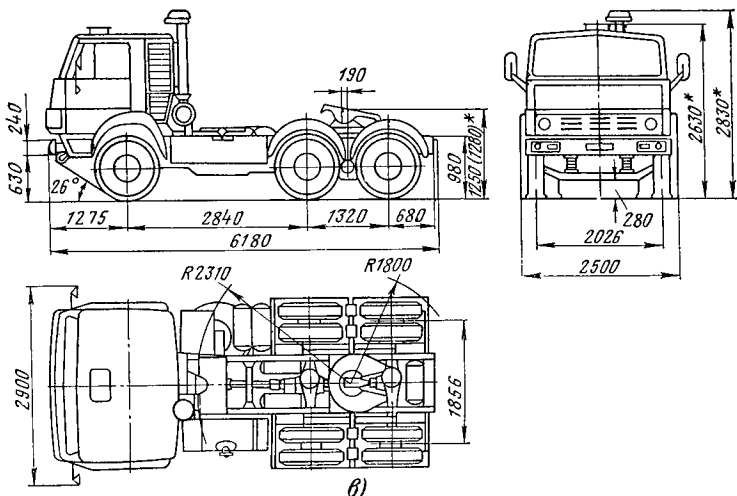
а — седельного тягача КамАЗ-5410 и седельного тягача КамАЗ-54112 (размеры даны для автомобиля полной массы, размеры со звездочкой — для снаряженного автомобиля)
